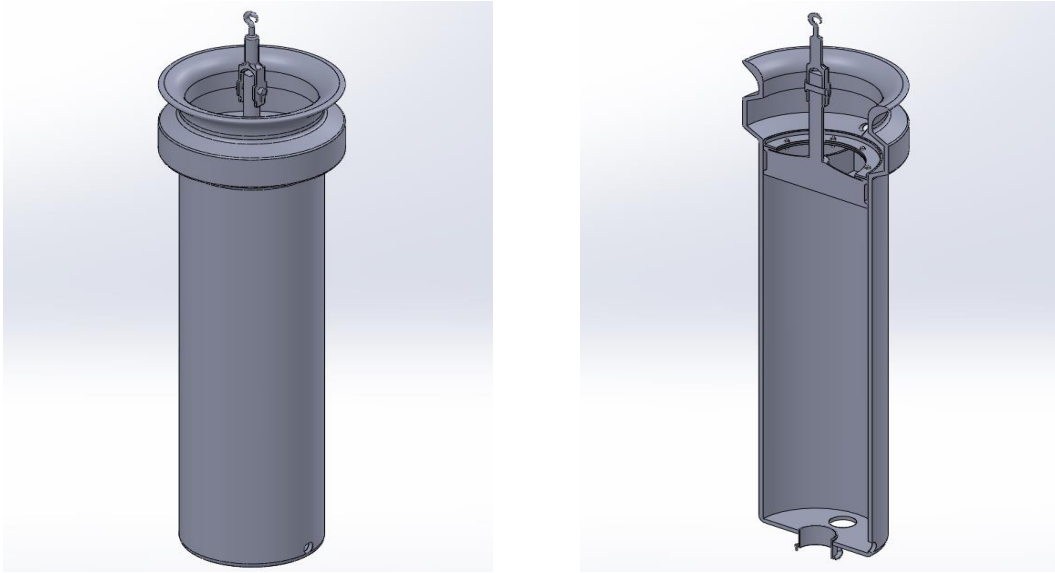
Sub-ensamblaje 01-01-00, respectivo al Cilindro Principal de la máquina de vapor de Newcomen. Vista general completa (izquierda) y vista general de sección (derecha).
